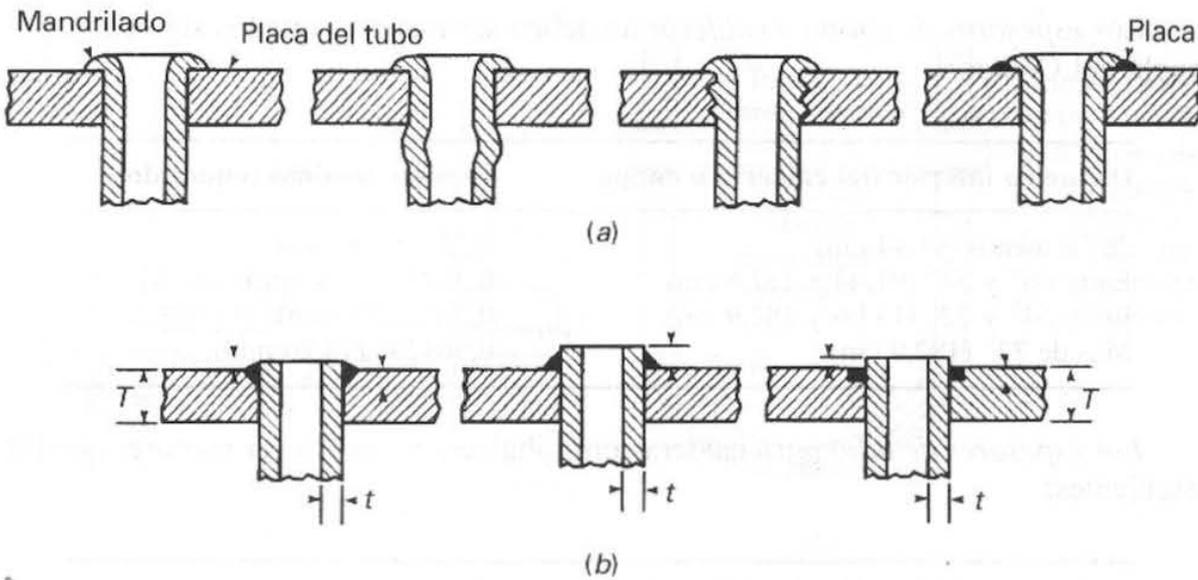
Fijaciones de los tubos de humos permitidas por el Código. (a) Tubos laminados y mandrilados en calderas pirotubulares. (b) Tubos laminados y soldados en calderas pirotubulares. Véase el Código para dimensiones de soldadura y sobre dimensionado del tubo y alojamiento en placa.
